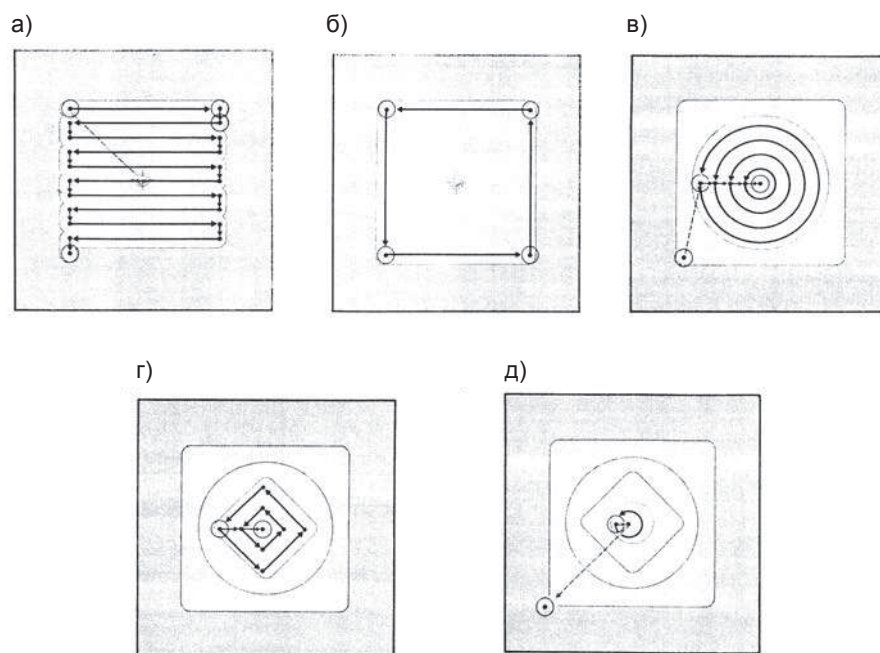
Схемы фрезерования внутреннего контура детали пальцевой фрезой: а) построчное фрезерование; б) фрезерование контура квадрата, в) построчное, круговое фрезерование плоскости круга, г) фрезерование плоскости квадрата, д) фрезерование плоскости и контура диаметром 10 мм
